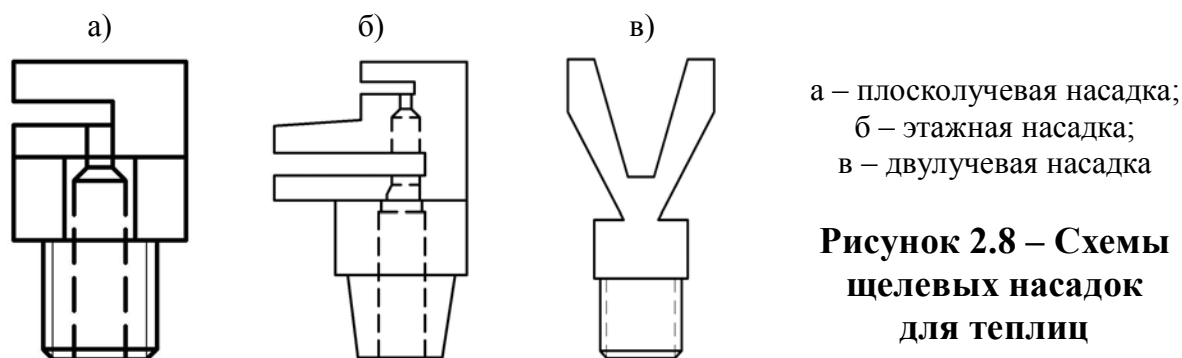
Схемы щелевых насадок для теплиц
